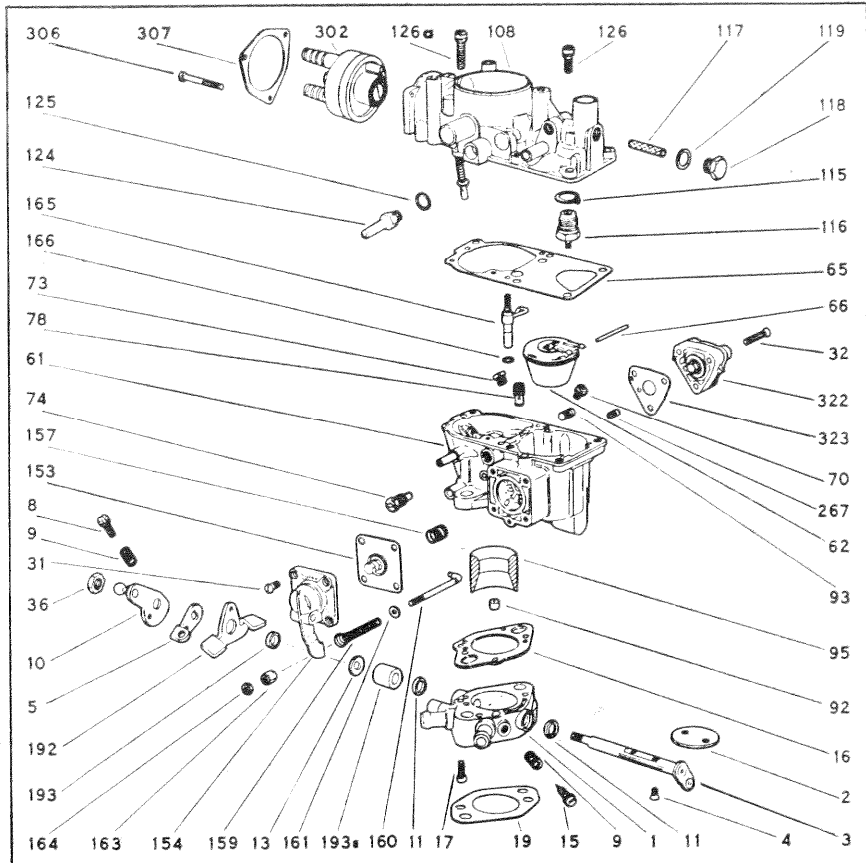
Vue éclatée du carburateur Solex 32 DITA 3
